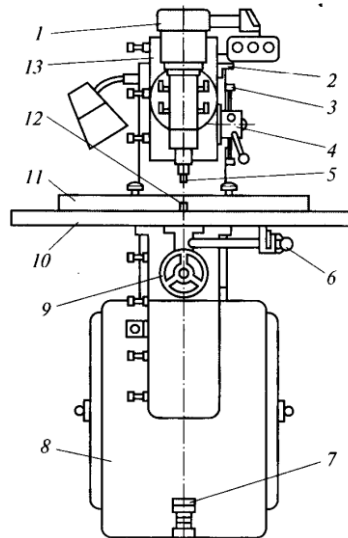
Одношпindelний фрезерний верстат з верхнім розташуванням шпинделя: 1 – електрошпиндель; 2 – упор; 3 – гвинт-обмежник; 4 – поворотна головка; 5 – фреза; 6 – ручка; 7 – педаль; 8 – станина; 9 – маховичок; 10 – стіл; 11 – напрямна лінійка; 12 – палець; 13 – супорт
